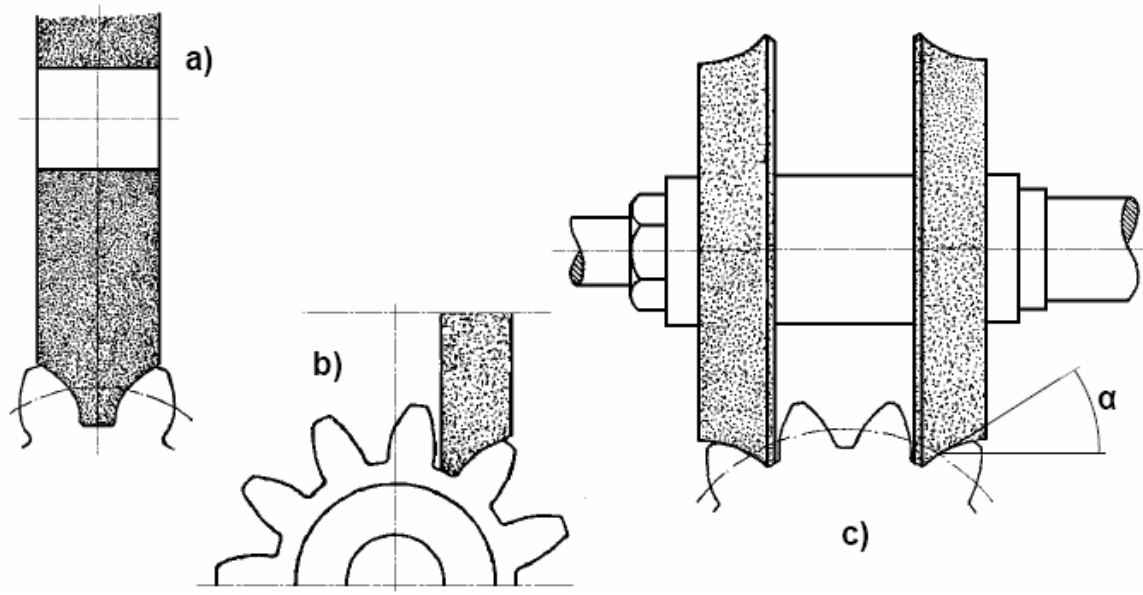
Tvarová bruska typu Orcut na ozubení [5]
